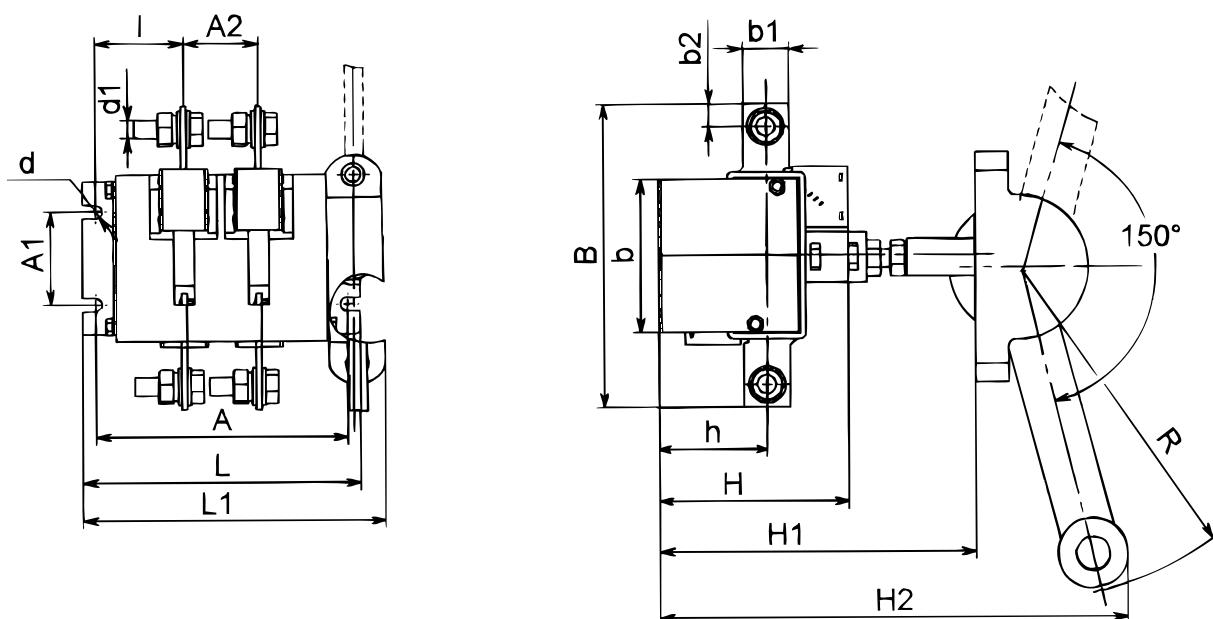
Выключатель-разъединитель на одно направление двухполюсный с передней смещенной рукояткой
